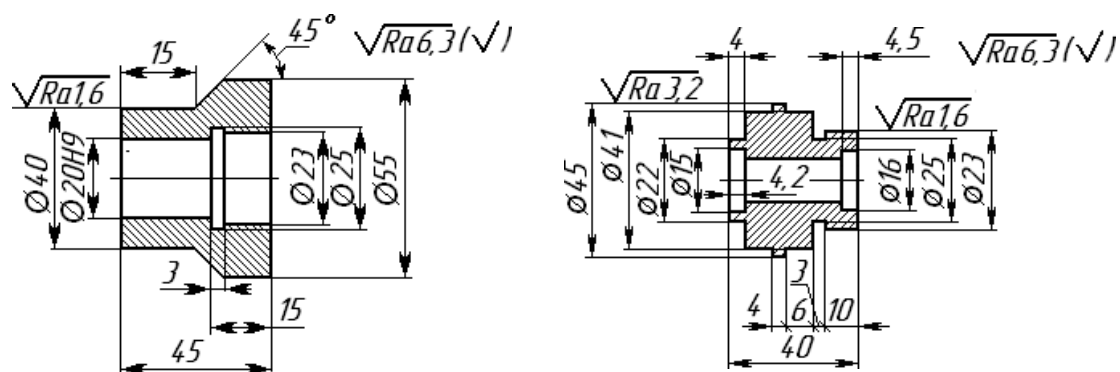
Типовые детали, обрабатываемые на токарно-револьверных станках
